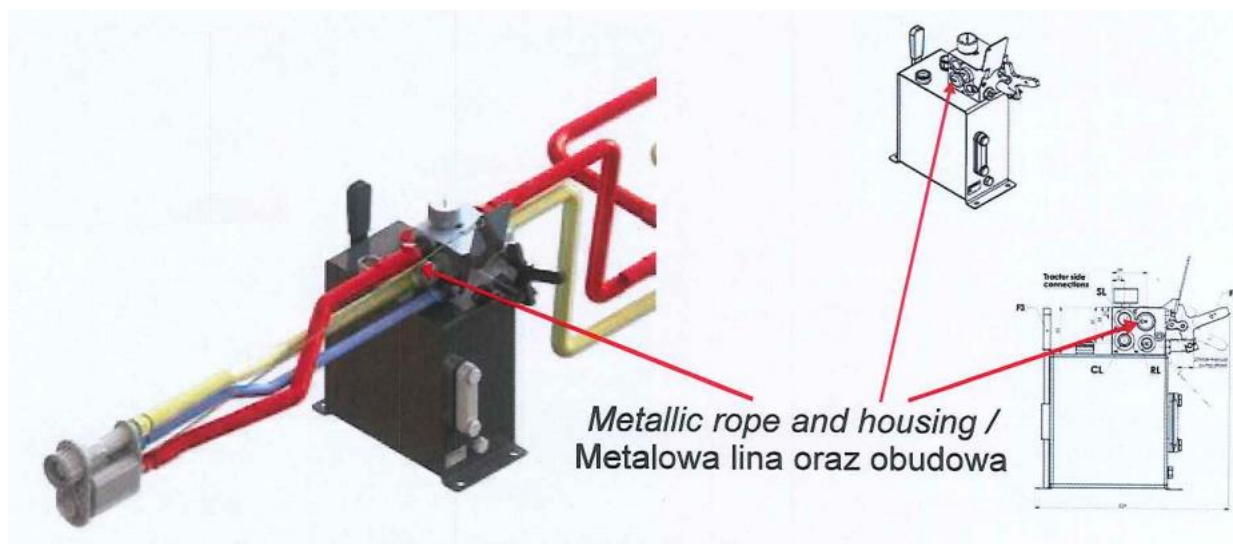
Rzut przedstawiający złącza od strony ciągnika
